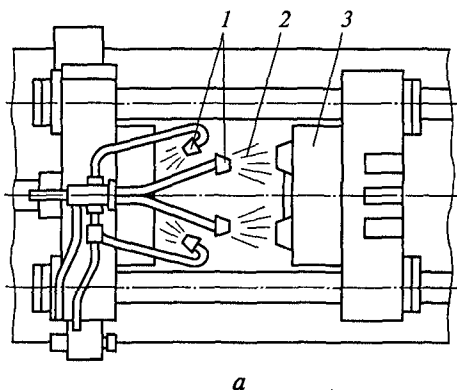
Устройства для автоматического смазывания пресс-форм:
